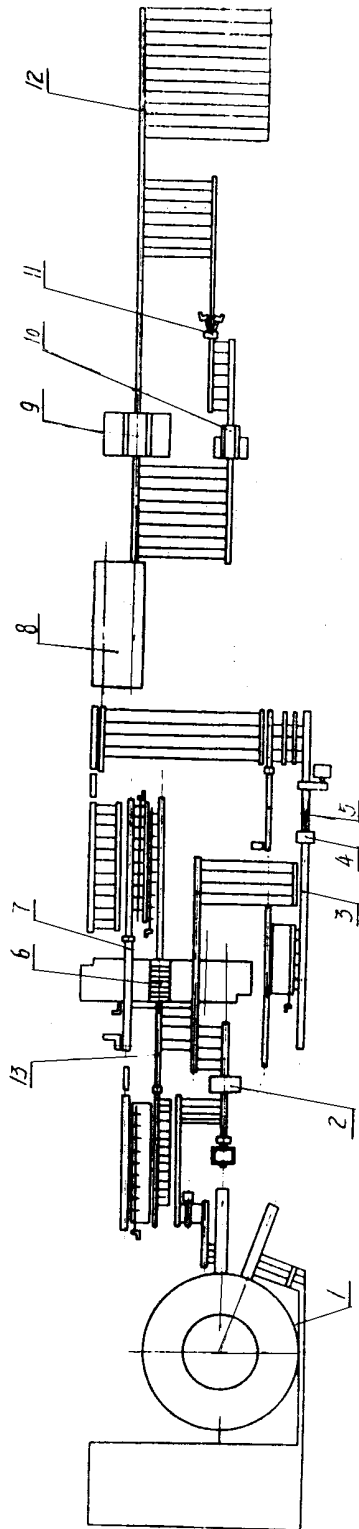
美国巴布柯克柯克斯公司连轧管机组平面图
